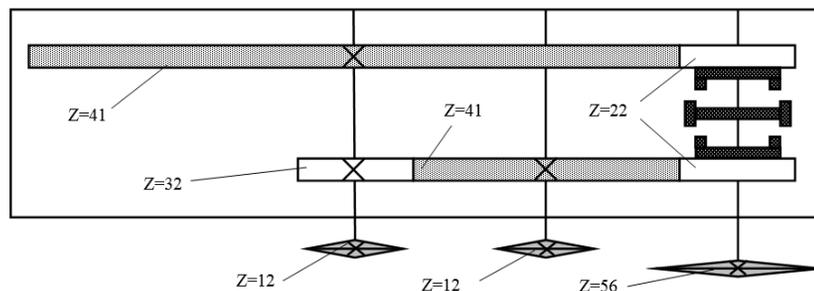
Кинематическая схема реверс-редуктора "Волгарь-5"
